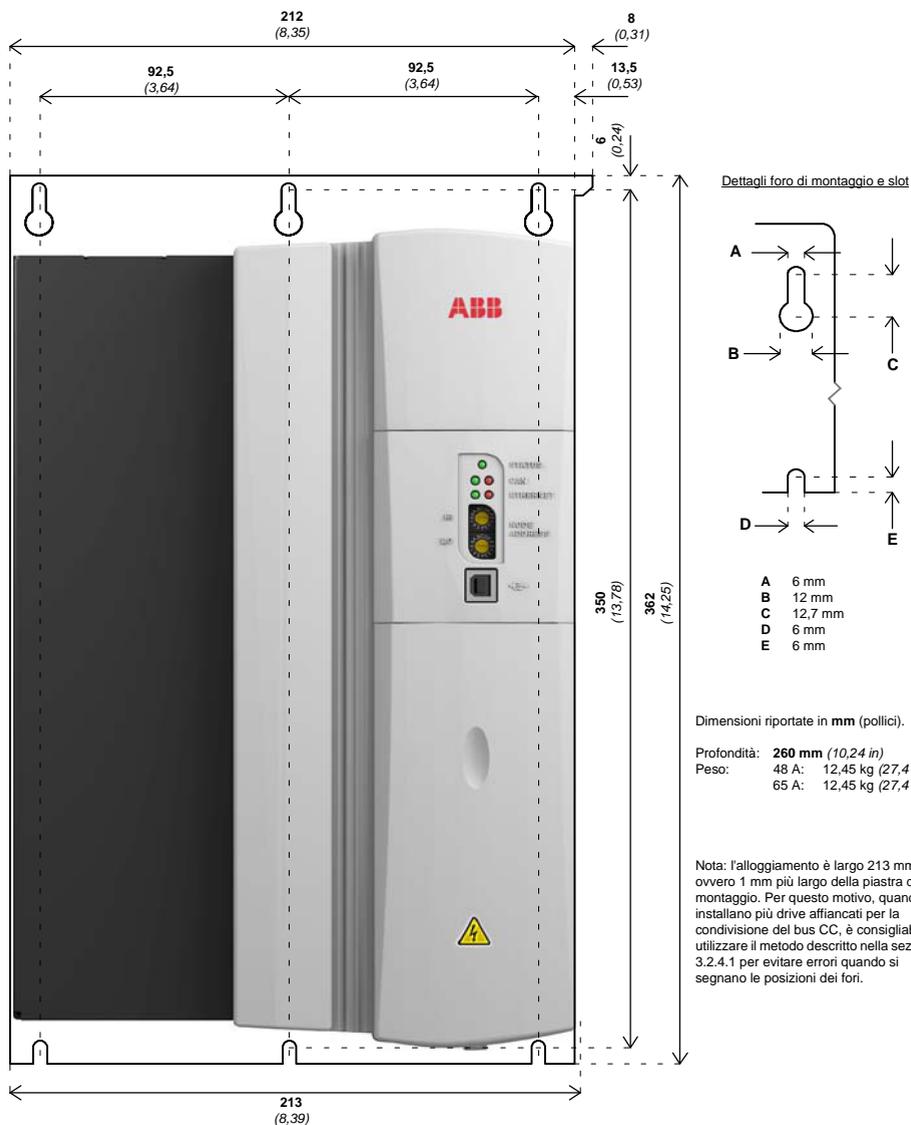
Dimensioni complessive e di montaggio - modelli a 48 A ~ 65 A
